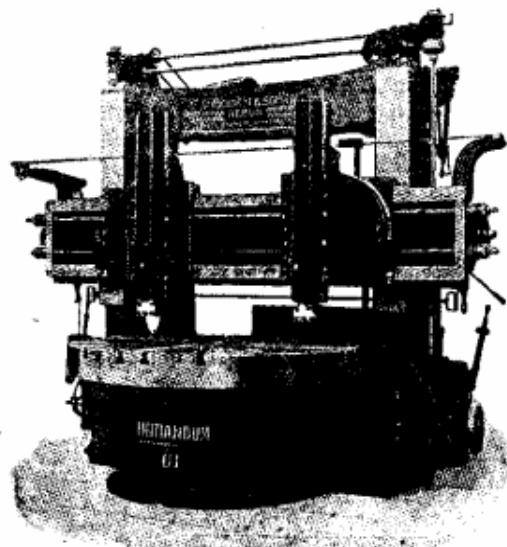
Вертикально-токарный и фрезерный станок карусельного типа.
